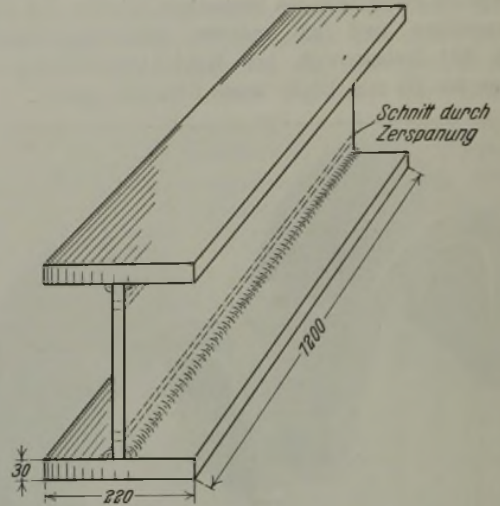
Entnahme von Aufschweißbiegeproben aus einem Versuchskörper.
